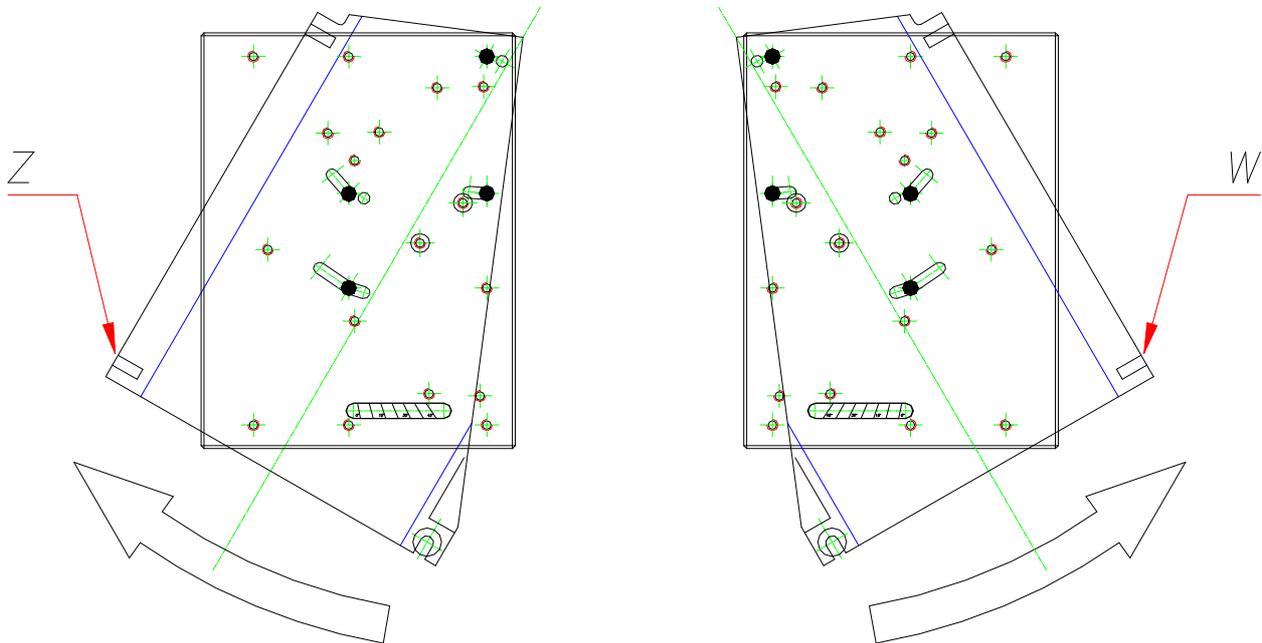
Крепление зажимов для первого шва Y-тройников 45° и 60°
